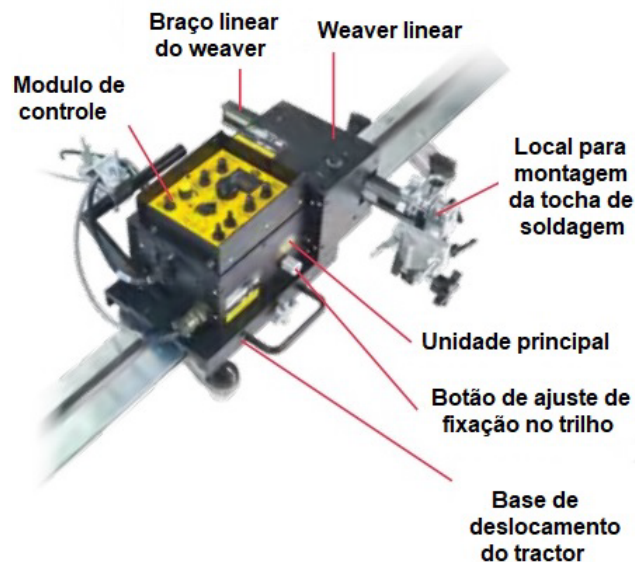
Layout do robô de solda linear do Sistema BUG-O MDS-1005.
